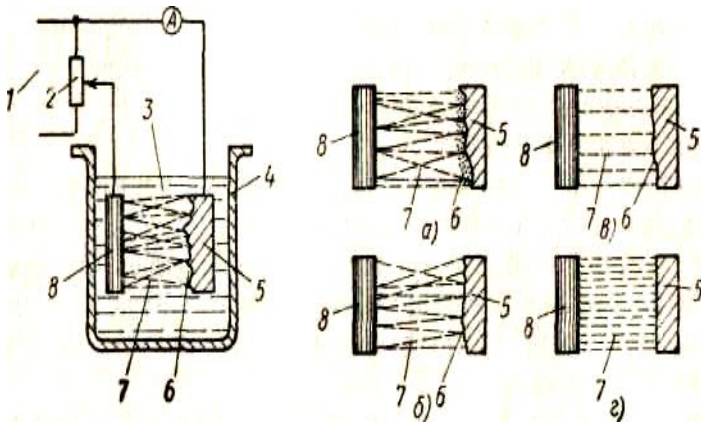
Схема електрохімічної обробки в стаціонарному електроліті: а) схема установки; б), д) послідовні стадії згладжування поверхні; 1 – джерело струму; 2 – резистор; 3 – електроліт; 4 – ванна; 5 – заготовка; 6 – плівка продуктів розчинення в западинах поверхні; 7 – силові лінії струму; 8 – катод
